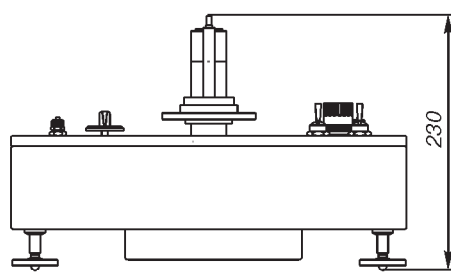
Калибратор давления пневматический 505 Воздух-II.
